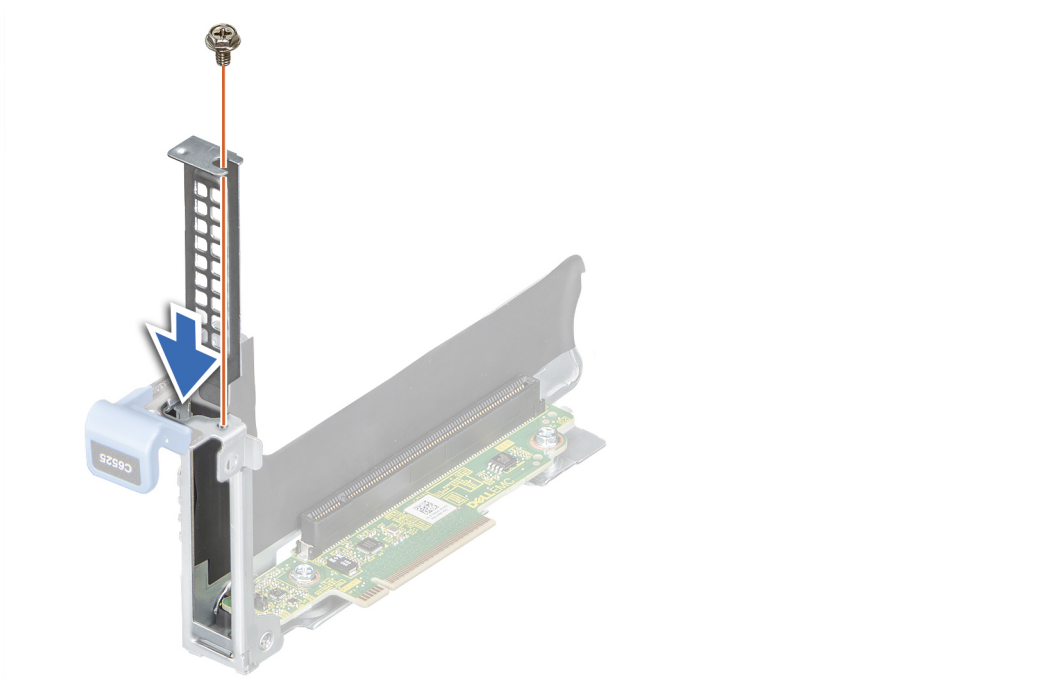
Installation de la plaque de recouvrement de la carte d'extension dans la carte de montage 1
